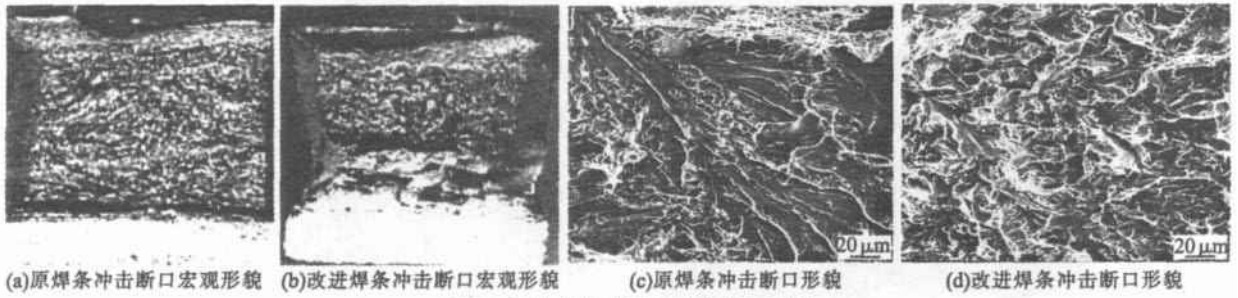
两种焊条典型的冲击断口形貌 Fig.2 The impact fracture surfaces of two electrodes
